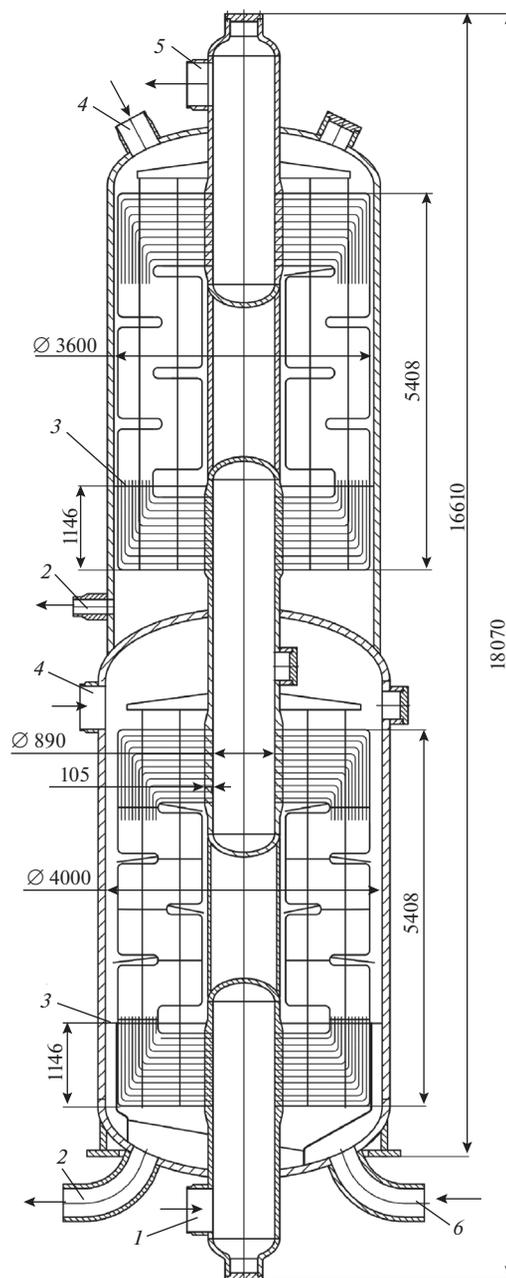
Сдвоенный подогреватель коллекторно-ширмового типа с трубными пучками из эвольвентных ширм в однониточном исполнении.
